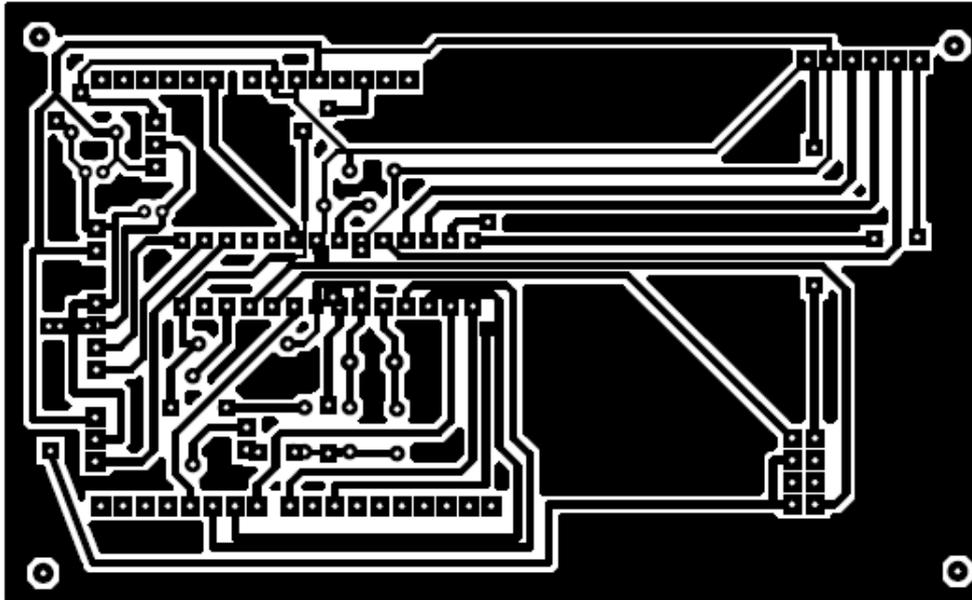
Placa PCB del circuito (El Autor, 2018)
